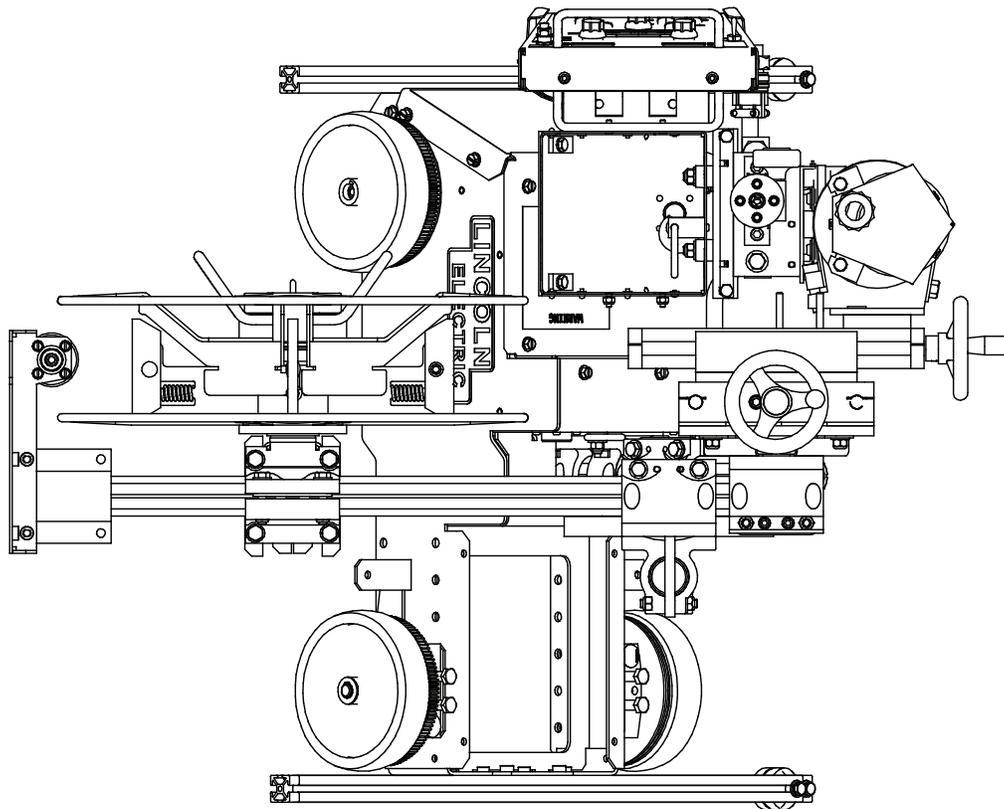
JUNTA PLANA VISTA DE TOPO
